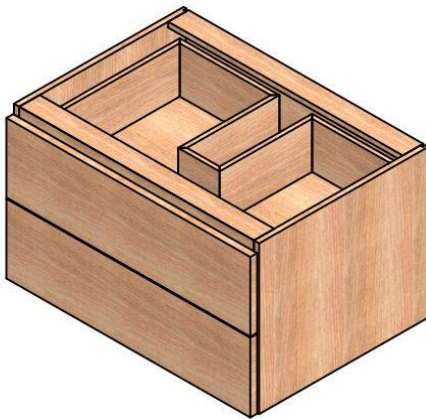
Mueble de baño lavabo de sobreencimera.
